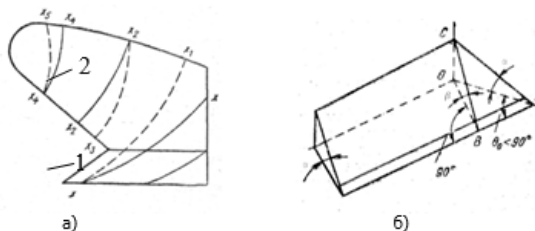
Рабочая поверхность корпуса плуга: а - сечения отвала поперечно-вертикальной плоскостью; б - кинетические параметры лемеха; 1 - лемех; 2 - отвал
